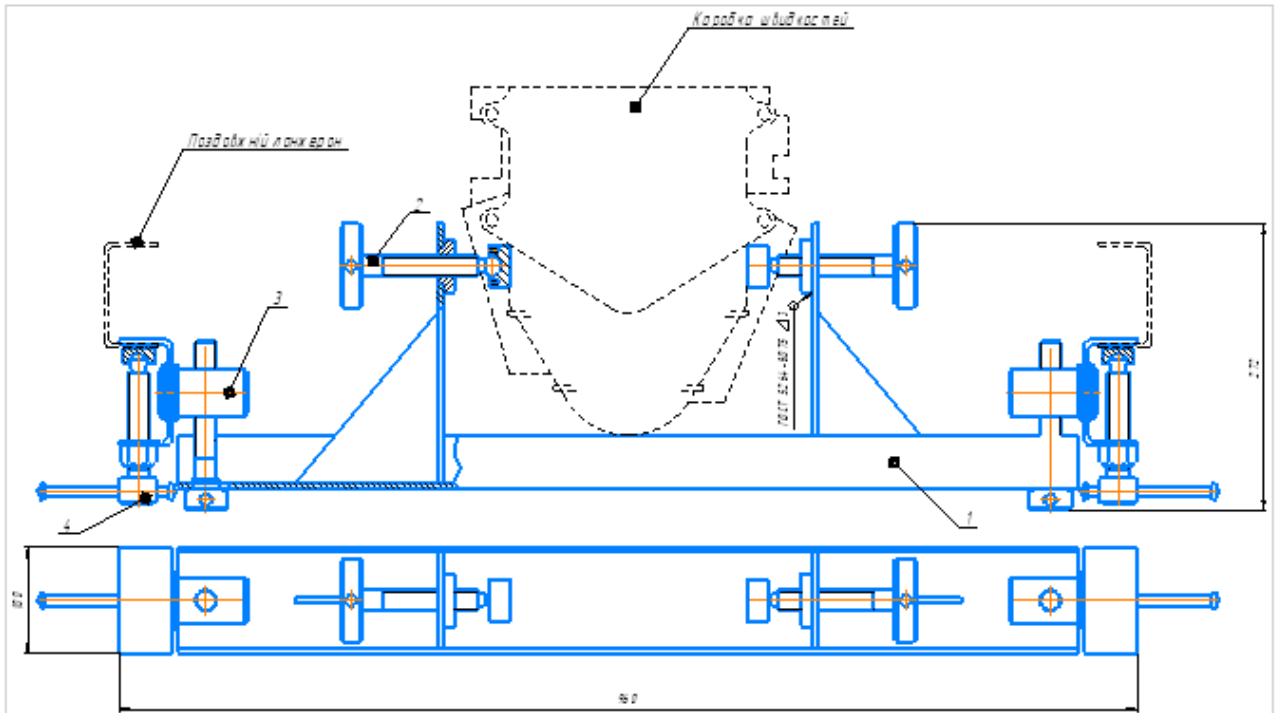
Обладнання для утримання і координування коробки передач складається з балки
